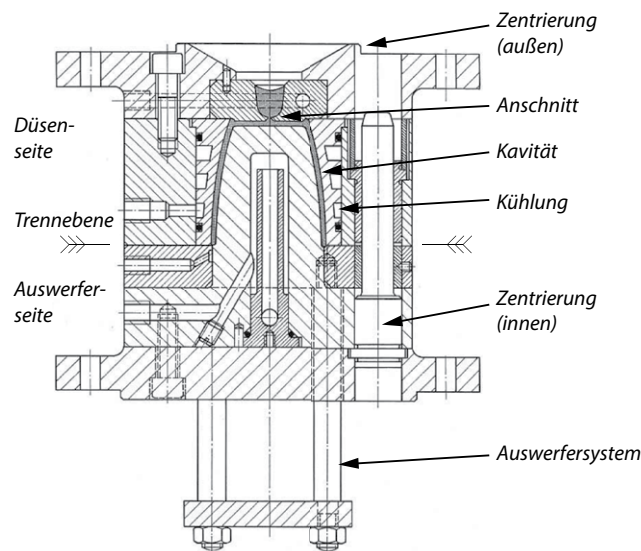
Schnitt durch ein einfaches Becherwerkzeug mit den wesentlichen Funktionen [Bildquelle: nach Menning, Werkzeuge für die Kunststoffverarbeitung]
